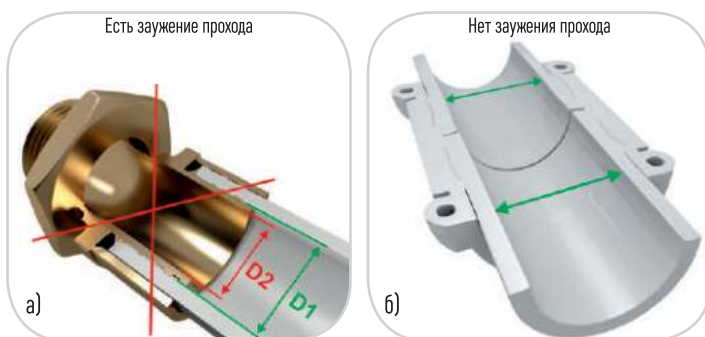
Сравнение компрессионного фитинга (а — есть заужение прохода) и сварного фитинга (б — нет заужения прохода)
